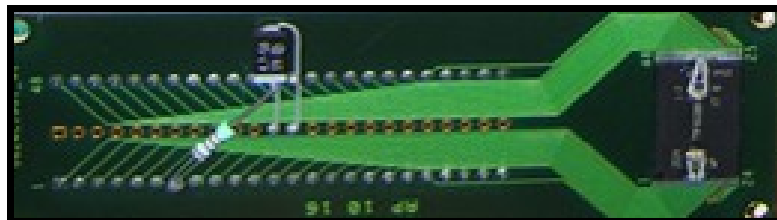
Photographie de la mémoire soudée sur le PCB.
